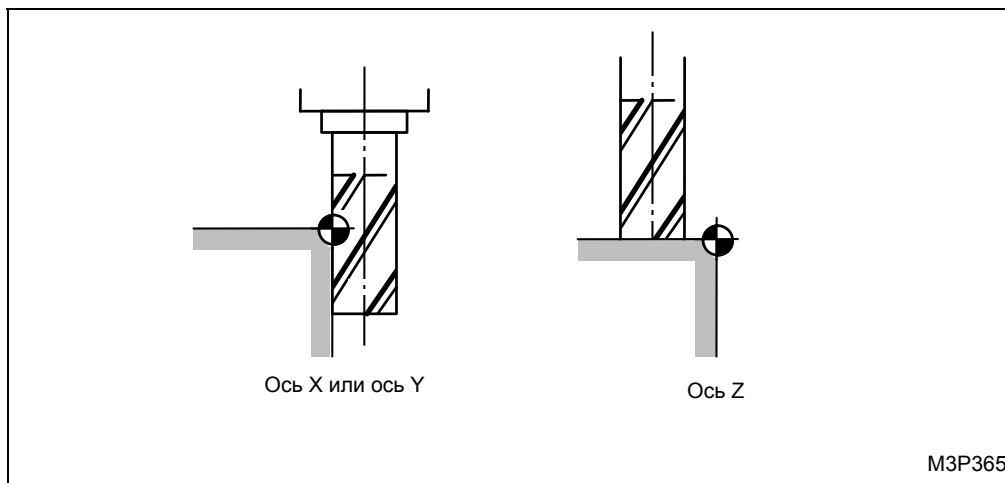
Инструмент в контакте с поверхностью заготовки
